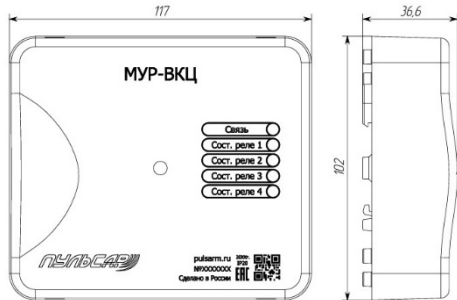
Габаритные размеры и маркировка МУР-ВКЦ (модель 2)
